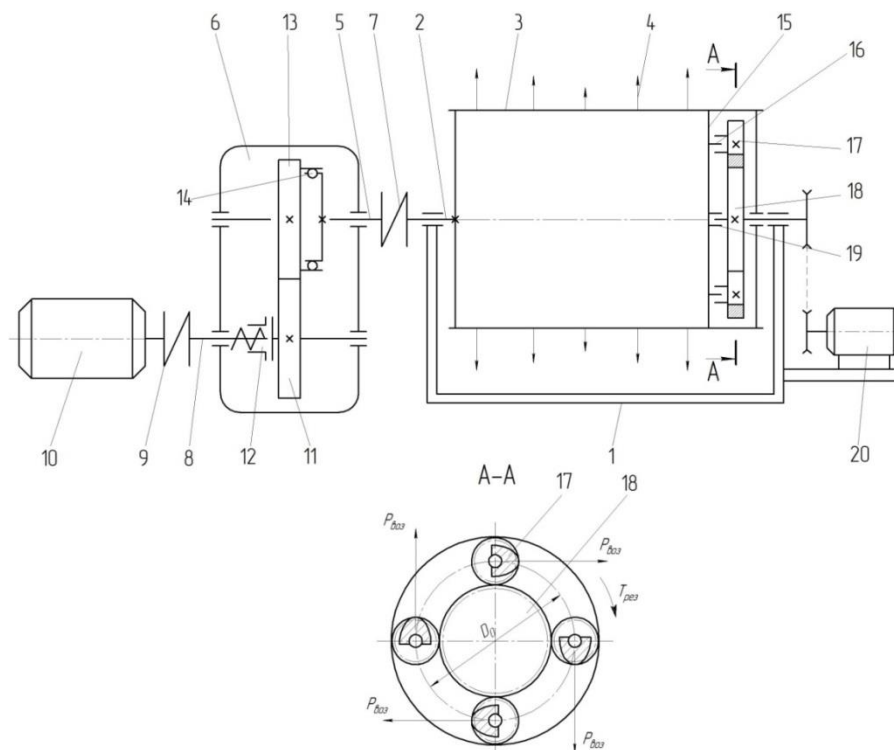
Конструкция машины с обгонной фрикционной и предохранительной муфты: 1 – рама; 2 – вал привода; 3 – барабан; 4 – зуб; 5 – ведомый вал; 6 – одноступенчатый цилиндрический редуктор; 7 – муфта; 8 – ведущий вал; 9 – муфта; 10 – двигатель; 11 – ведущее зубчатое колесо; 12 – предохранительная муфта; 13 – ведомое зубчатое колесо; 14 – обгонная фрикционная муфта; 15 – кронштейн; 16 – ось; 17 – зубчатое колесо с дебалансом; 18 – зубчатое колесо; 19 – опора вращения; 20 – привод зубчатого колеса 18
